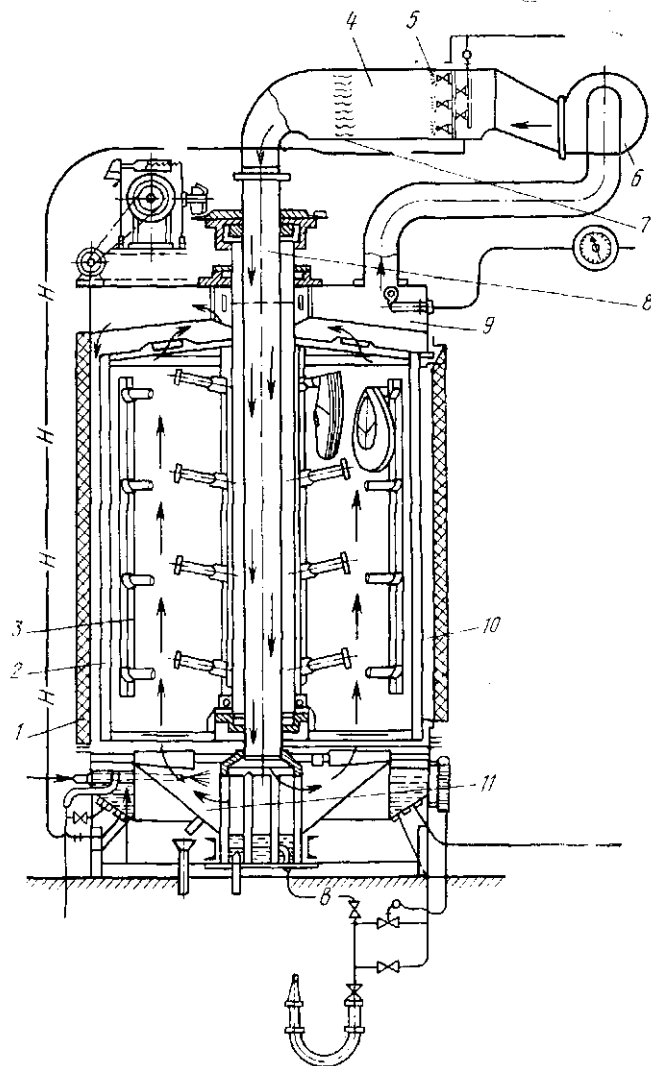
Схема роторной установки для увлажнения заготовок верха обуви
